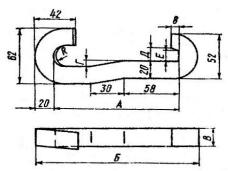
Противоугон самозаклинивающийся (в скобе): I - скоба; 2 - клин
